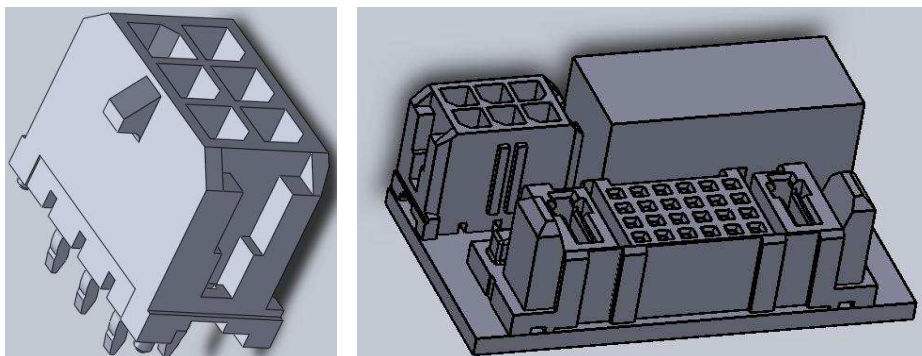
Modelado de un componente (a la izquierda) y modelado del ensamblaje de una placa (a la derecha)
